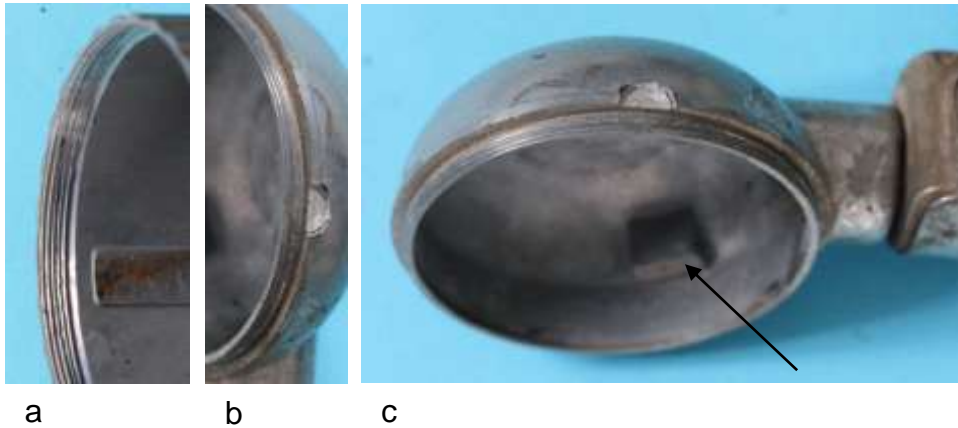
Versraubung der Gehäuseteile: a) Innengewinde des Gehäusetopfes, b) Außengewinde der Bodenschale, c) Auflage für den Anker
